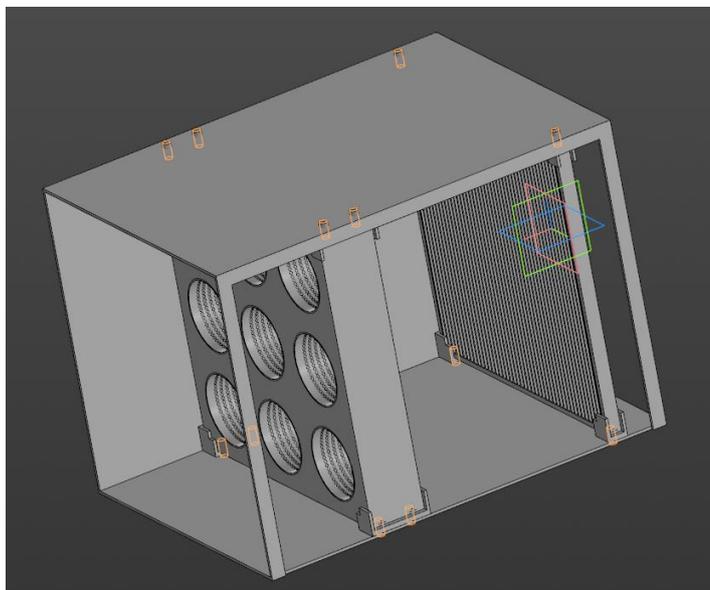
Корпус фильтра с установленным фильтром абсорбирующего типа
